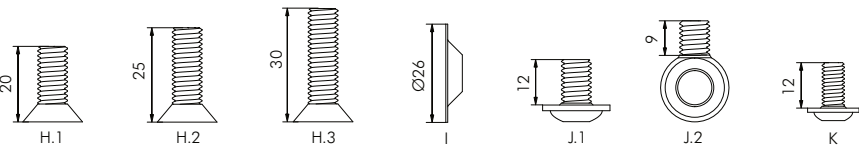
Schrauben (Länge in Millimeter, Darstellungmaßstab 1:2), für Teilebezeichnung siehe 2.)
